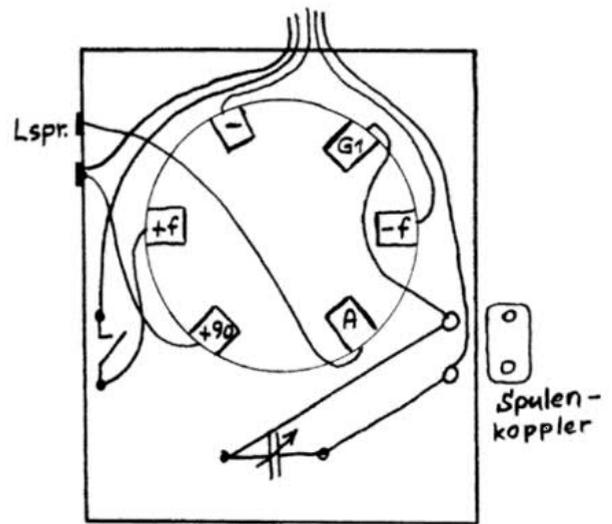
Die Innenverdrahtung beschränkt sich auf ein Mindestmaß.
